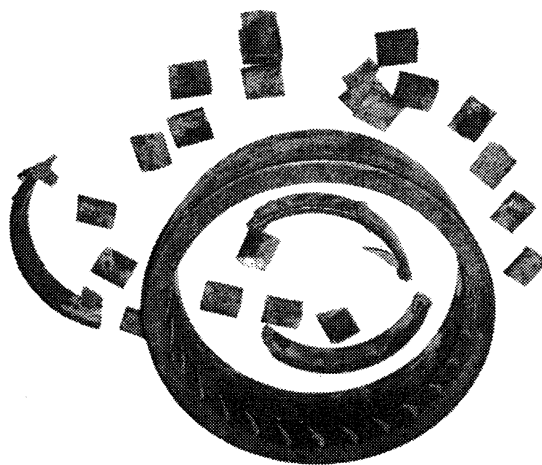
Отливка «Статор», разрушенный под воздействием ударных нагрузок, выполненный без БКЛ
